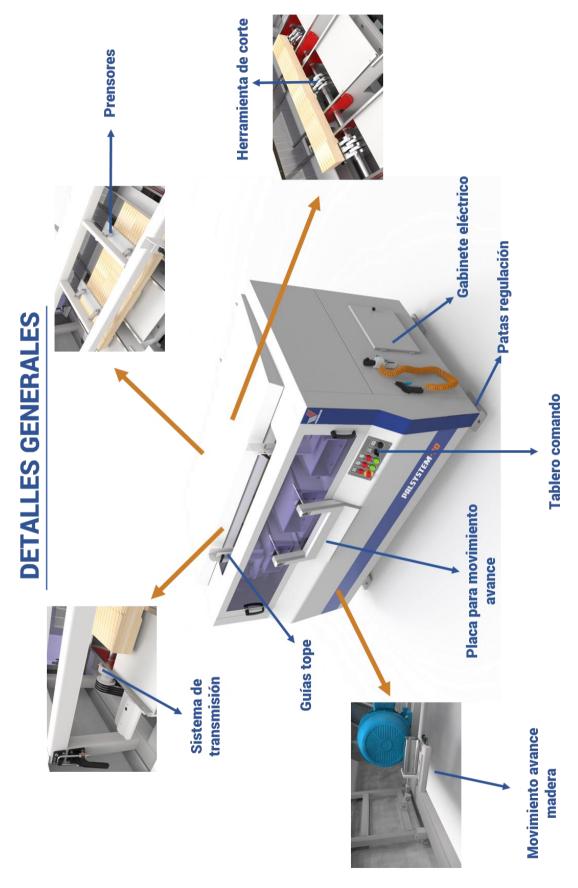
Detalles Generales (Fuente: elaboración propia)
